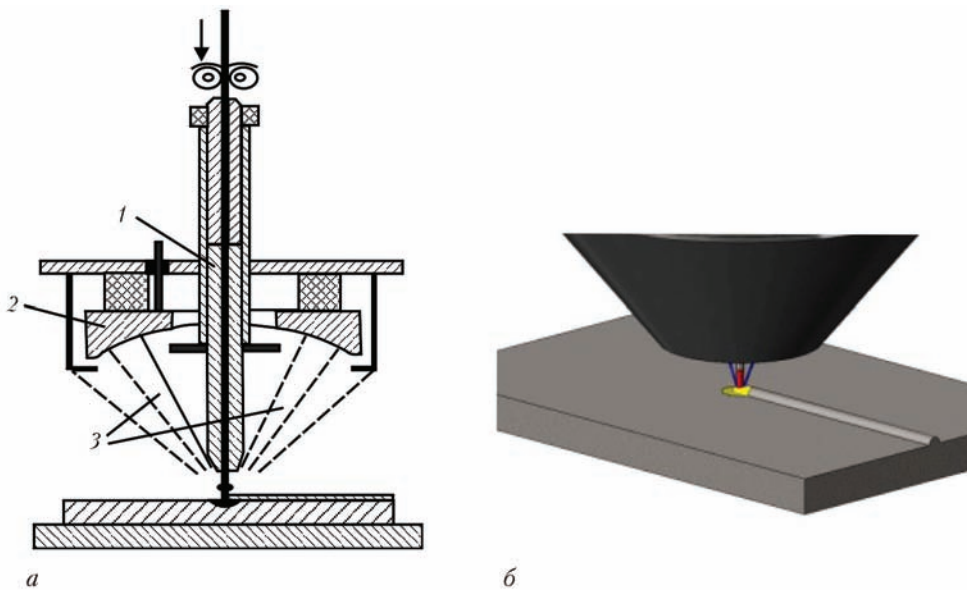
Схема установки для реализации технологии «xBeam 3D Metal Printing» (а) и процесса наплавки (б): 1 — направляющее устройство; 2 — катод; 3 — электронный луч
